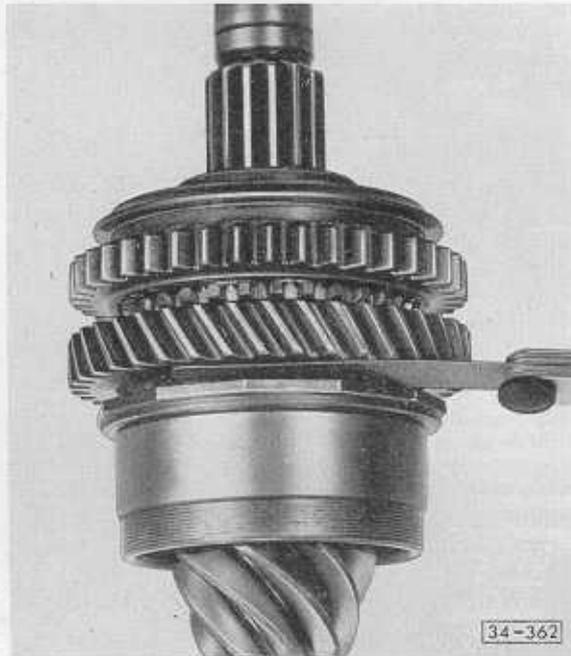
Axialspiel des Zahnrades für 1. Gang einstellen.
